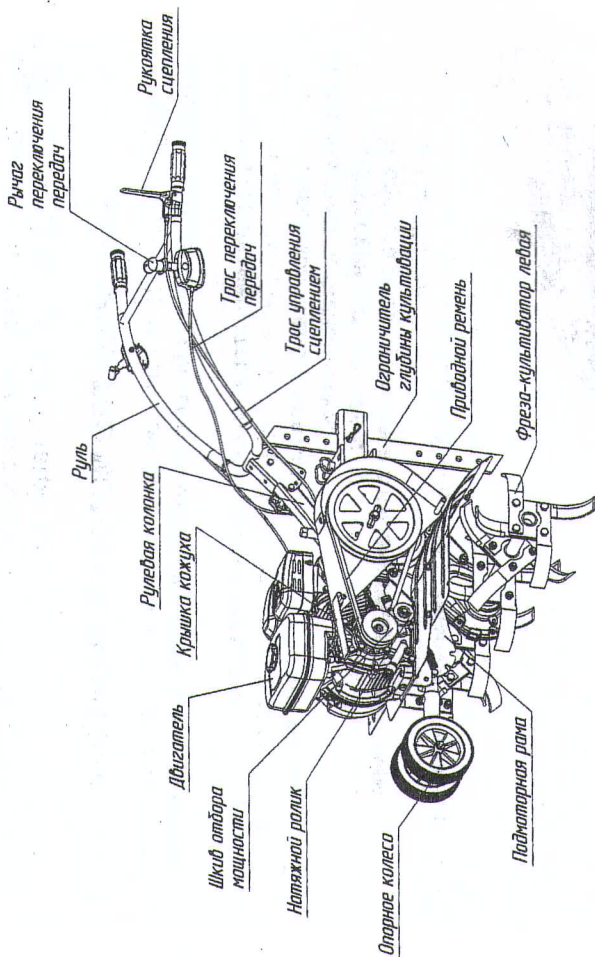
Мотокультиватор МК-200. Общий вид (вид слева, защитный кожух условно снят)
